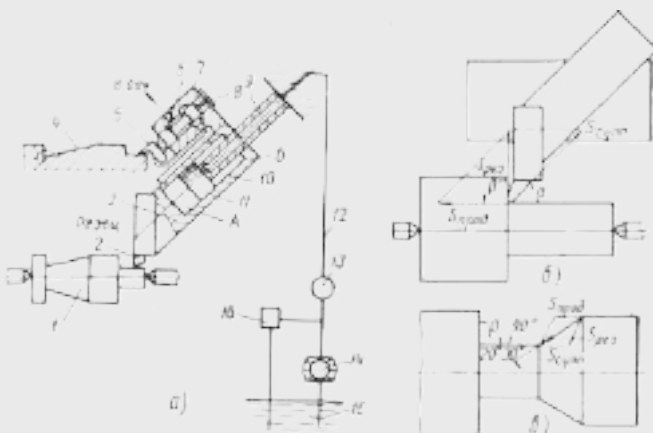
Схема роботи гідравлічного копіювального супорта: а — схема гідравлічної слідувальної системи; б — схема підрізки торця; в — схема обробки зворотного конуса.
